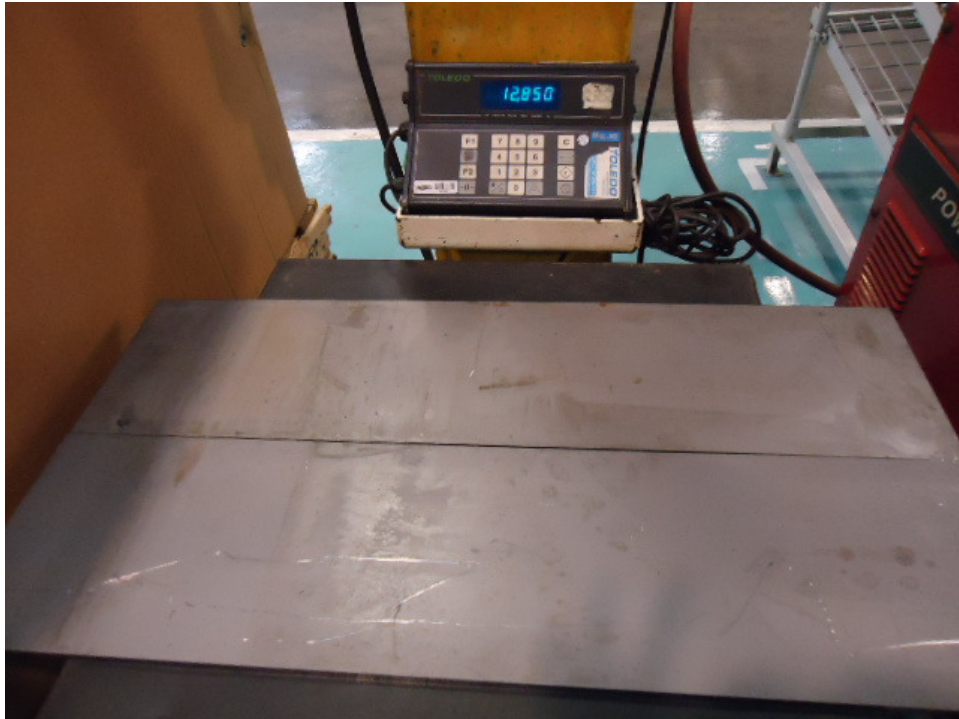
Chapa antes da soldagem com mistura 15% CO₂
